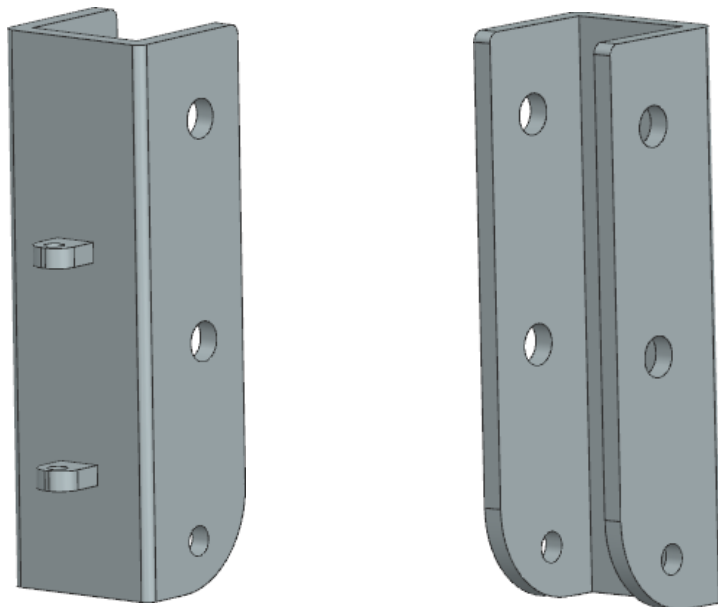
y 43. Diseño en CAD del diseño del cuerpo.
